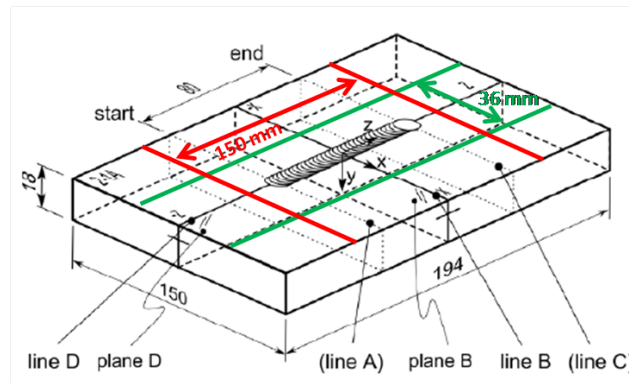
Maquette initiale soudée avant découpe pour analyse choc laser
